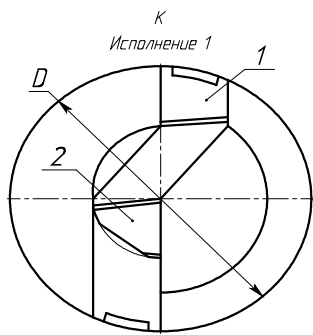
Профиль поперечного сечения сверла исполнения 1
